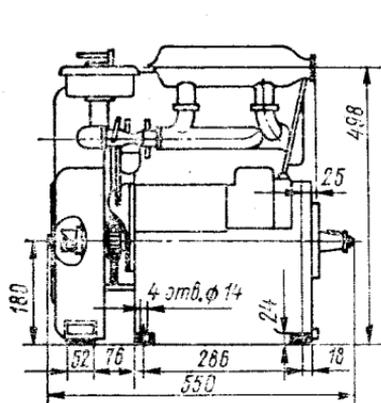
Габаритный чертеж четырехтактного двигателя «УД2-М1».
